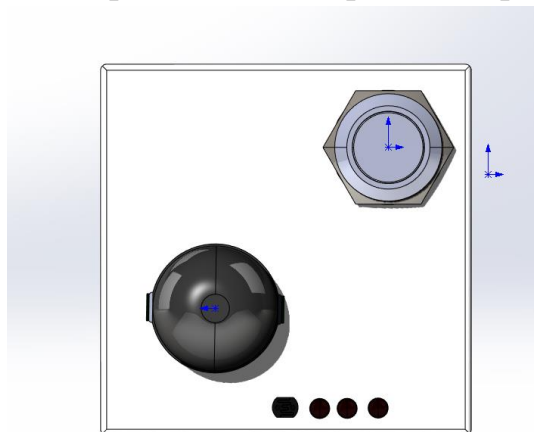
Вид зверху зібраного корпусу з платою
